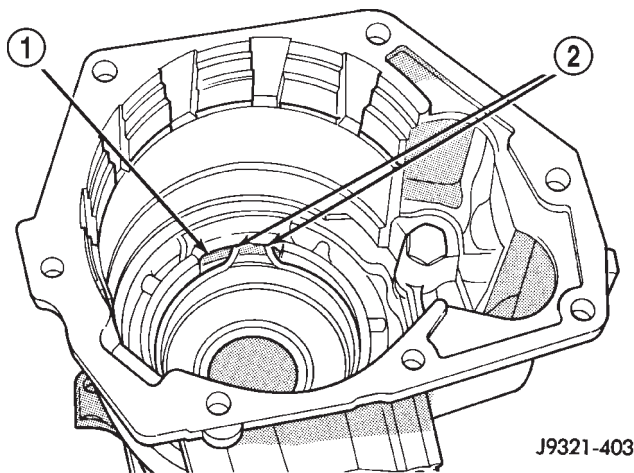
Richtig montierter Führungsring für hinteres Lager
